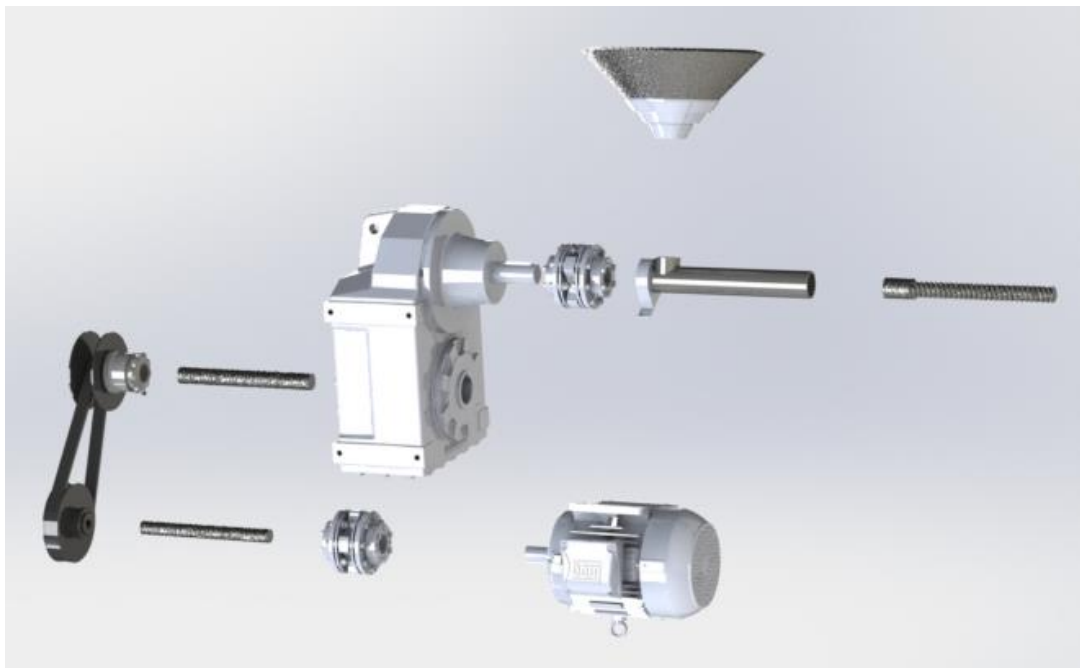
Modelado del sistema diseñado, en vista explosionada.
